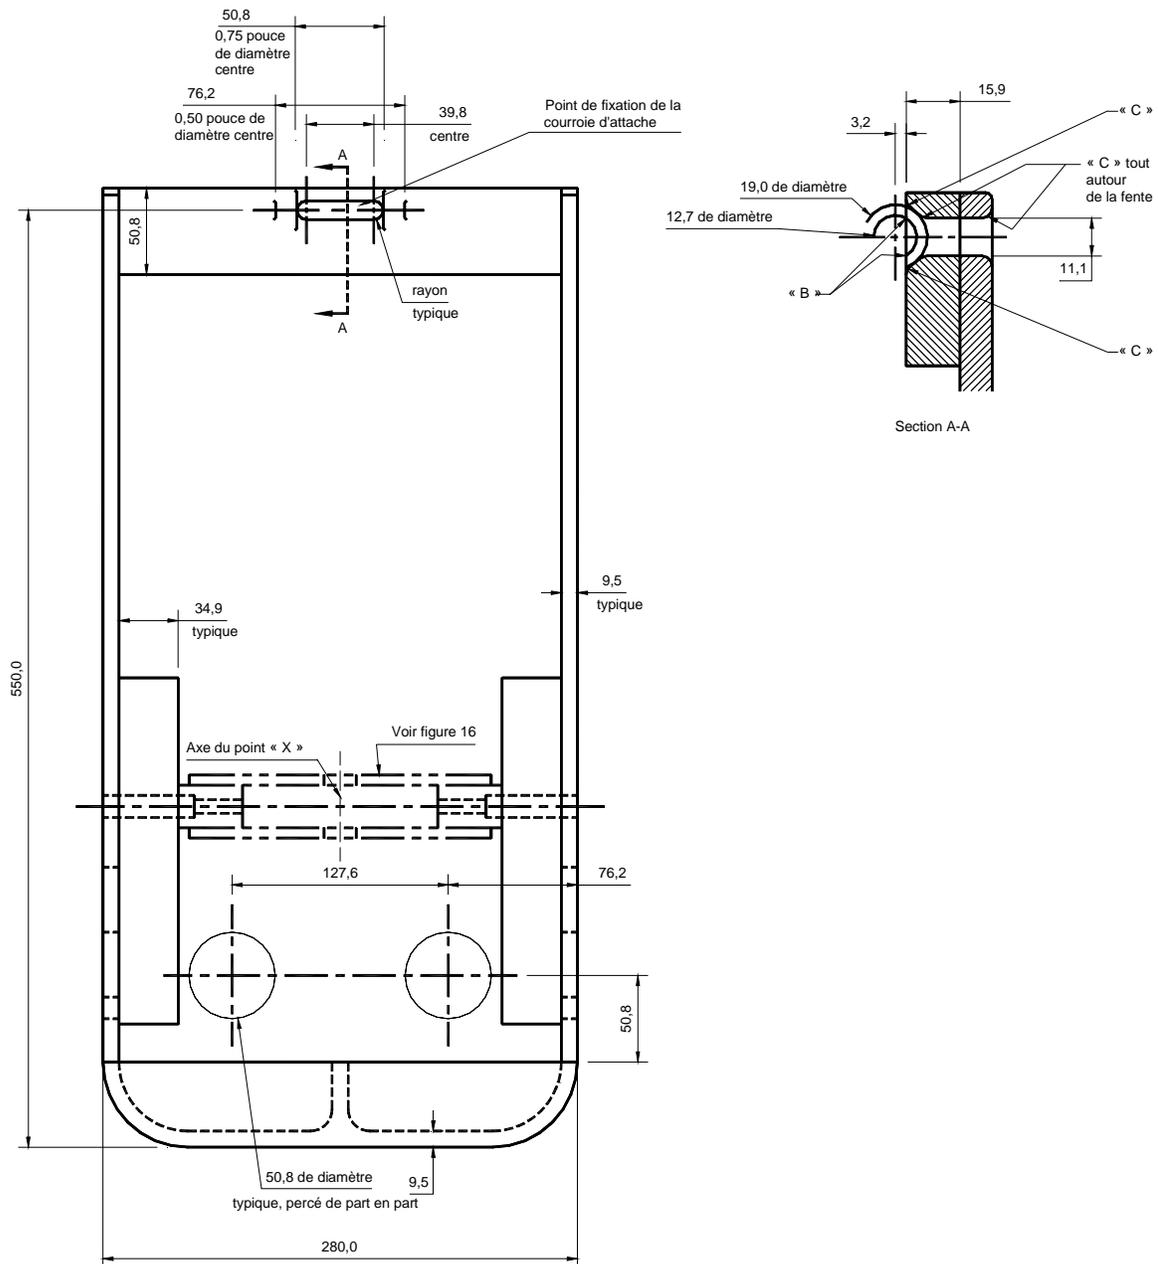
Vue en plan du dispositif d'essai d'application de la force statique
